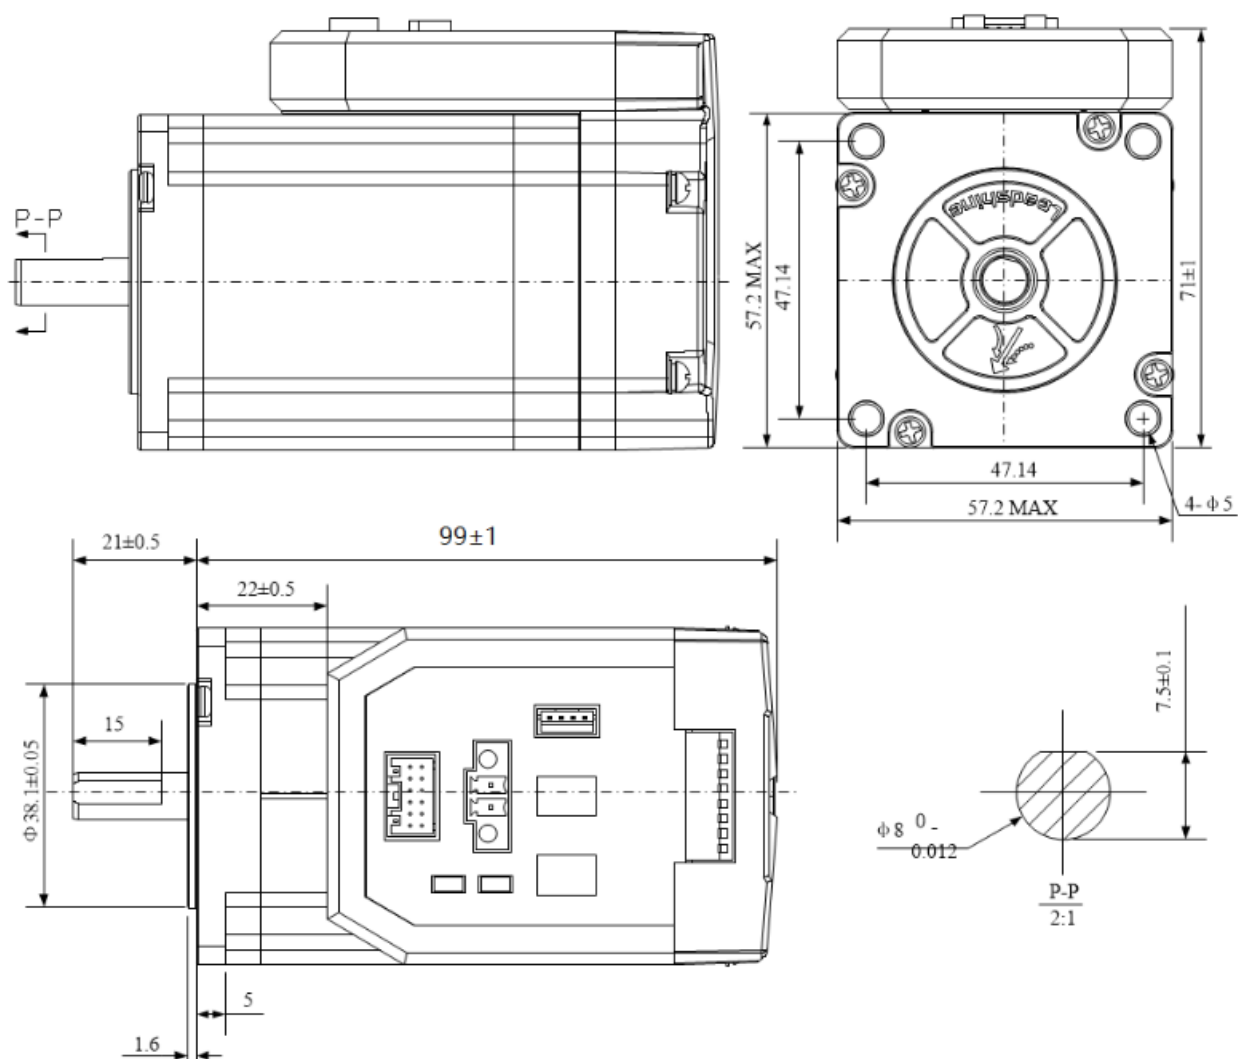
Габаритный чертеж привода iCS-RS2323.
